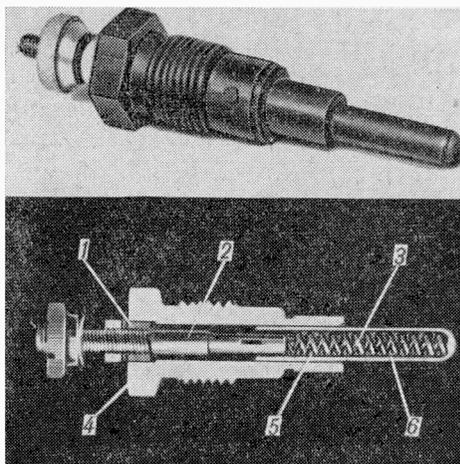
Свеча накаливания (вверху — общий вид, внизу — свеча в разрезе): 1 — уплотнительная прокладка, 2 — стержень свечи, 3 — керамический наполнитель, 4 — корпус свечи, 5 — нагревательная спираль, 6 — трубка спирали.
